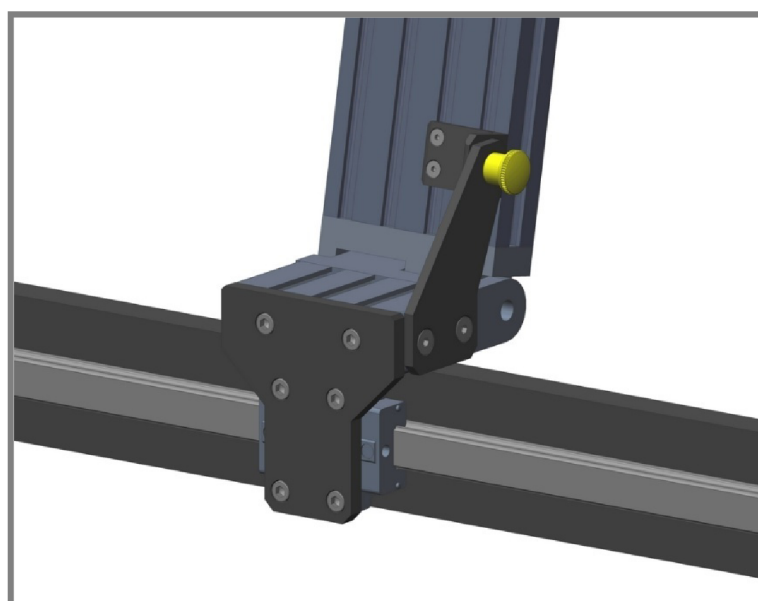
Varianta A-Suport s kluzným vedením [autor]
